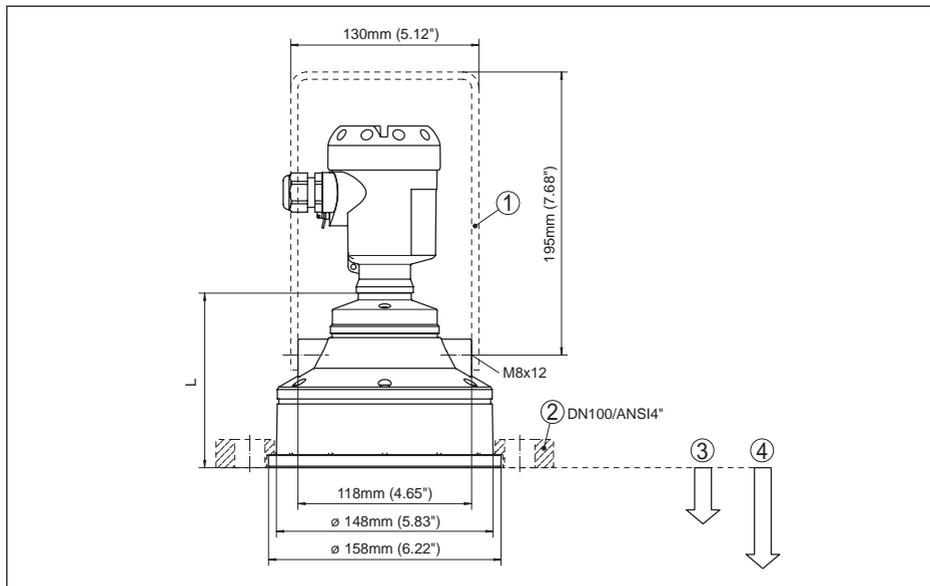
OPTISOUND 3030 C, размер L для корпуса из алюминия = 118 мм (4.646"), для корпуса из пластмассы = 112 мм (4.409"), для корпуса из нержавеющей стали = 107 мм (4.213")
